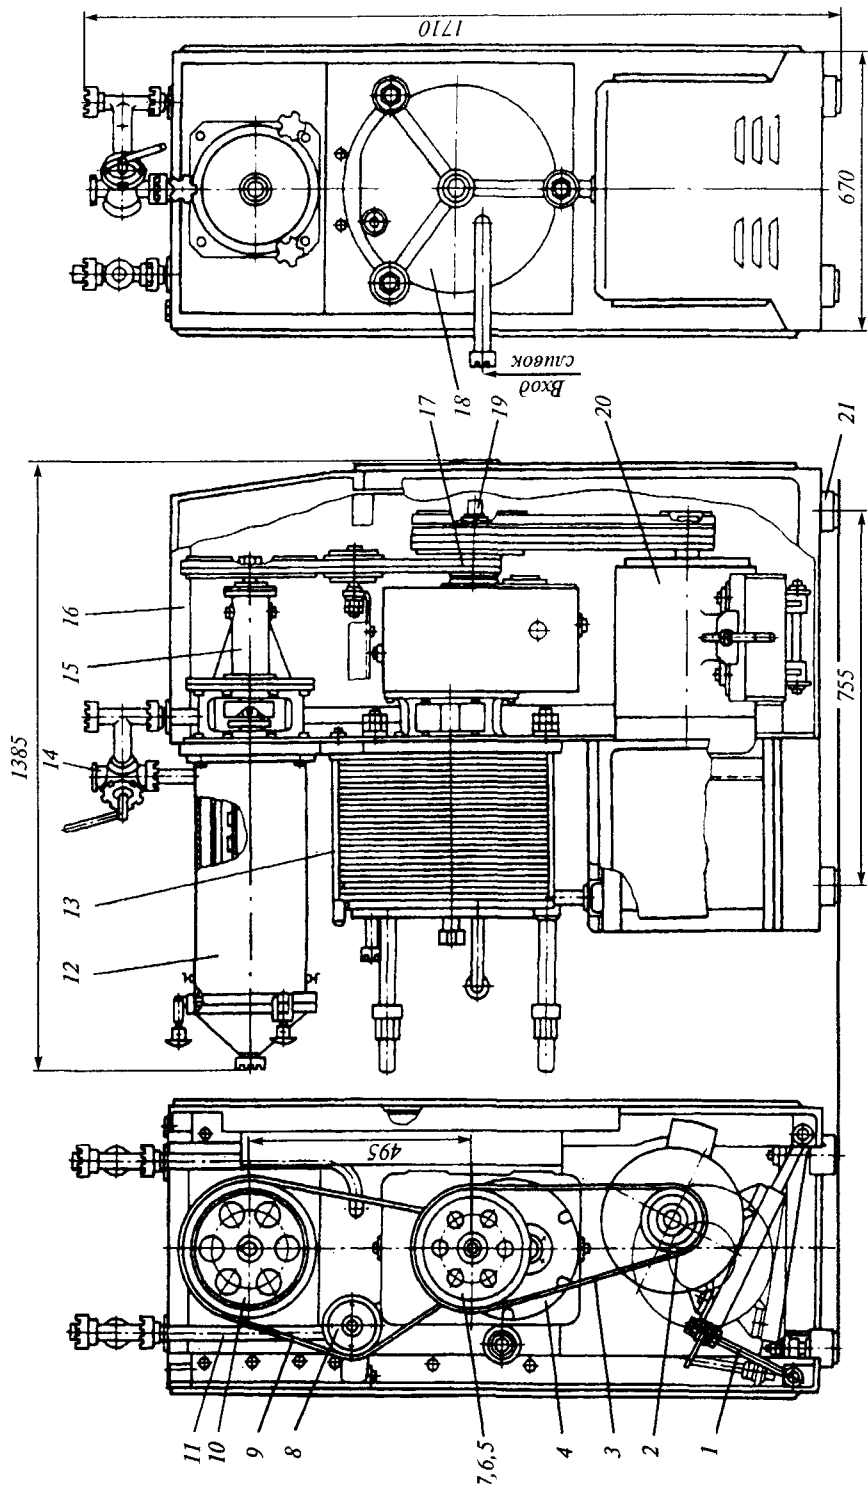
Пластинчатый маслообразователь РЗ-ОУА
